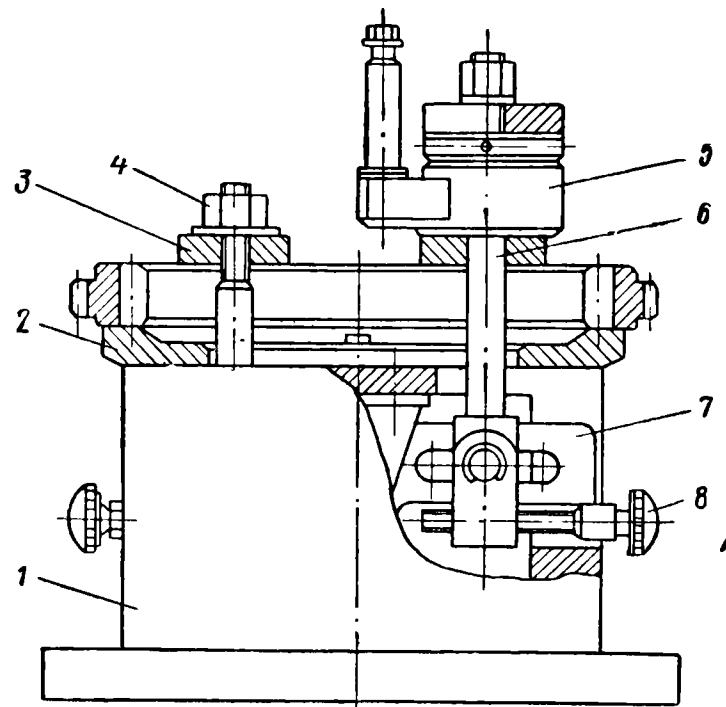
Конструкция УПТО для обработки зубчатых колес диаметром до 790 мм.
